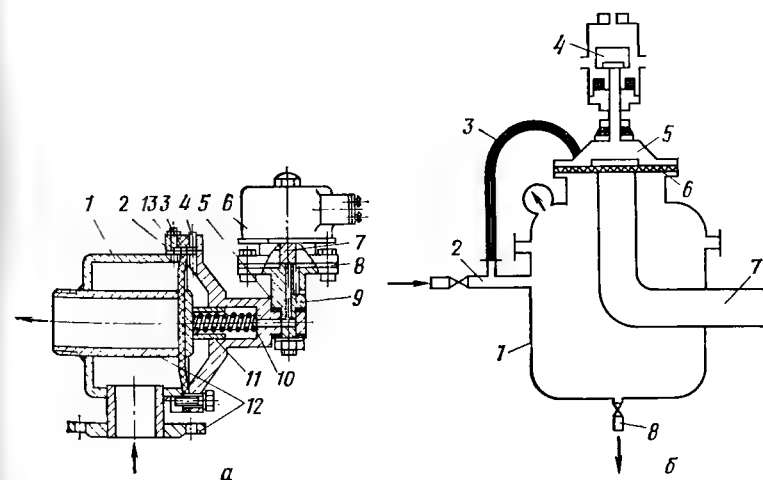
Устройство подачи сжатого воздуха для регенерации рукавов:
